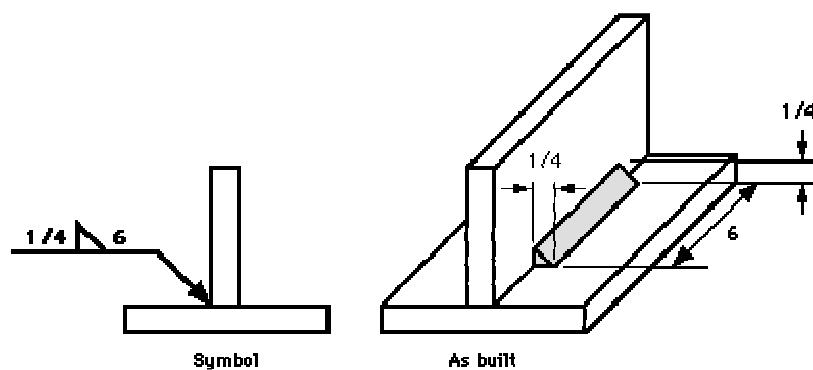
Aplicación de símbolos de soldadura de filete
